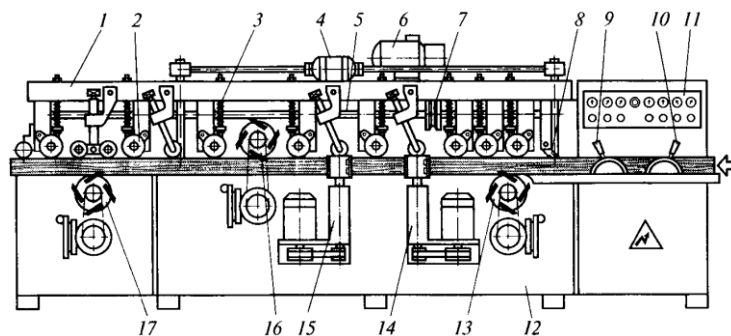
Чотирибічний поздовжньо-фрезерний верстат: 1 – траверса; 2 – приводний ролик; 3 – пружина; 4, 6 – електродвигуни; 5 – вал; 7 – варіатор; 8 – кігтевий захист; 9, 10 – рукоятки; 11 – пульт керування; 12 – станина; 13–16 – шпинделі; 17 – калювальний супорт
